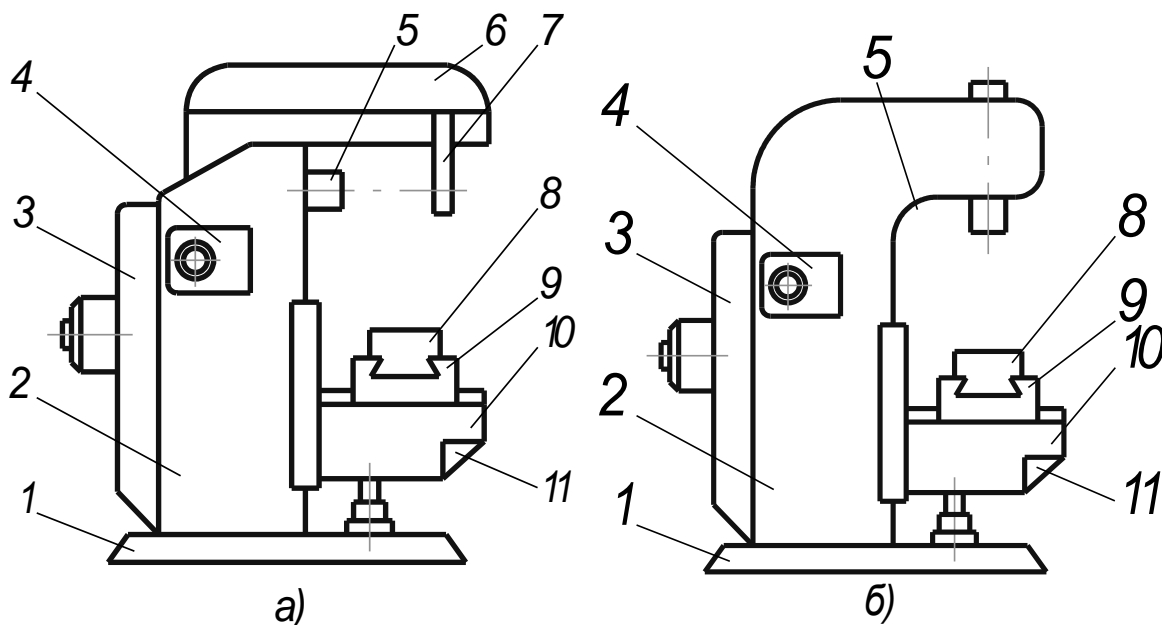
Схеми горизонтально-фрезерного (а) та вертикально-фрезерного (б) верстатів
